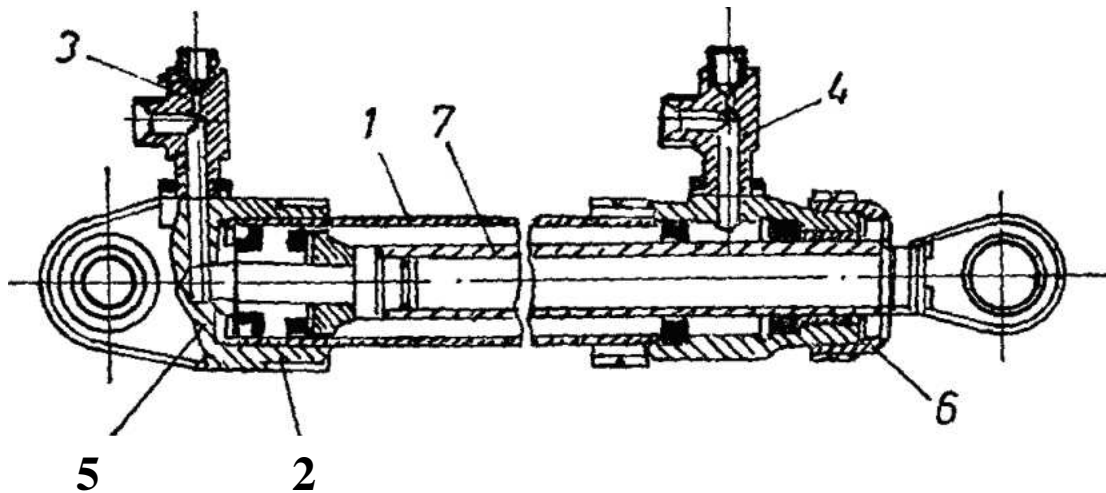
Motor hidraulic rectiliniu (cilindru de forță)
